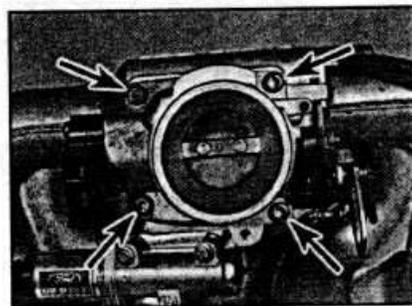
D.11. Расположение винтов крепления корпуса дросселей.
